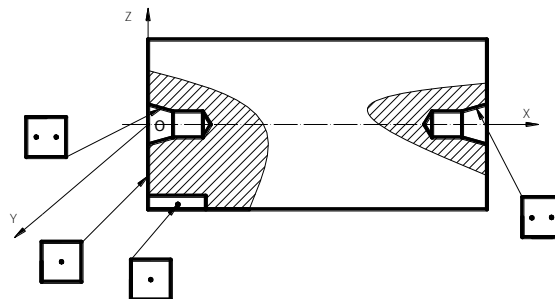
Схема установки детали на передний плавающий и задний жесткий центры.
